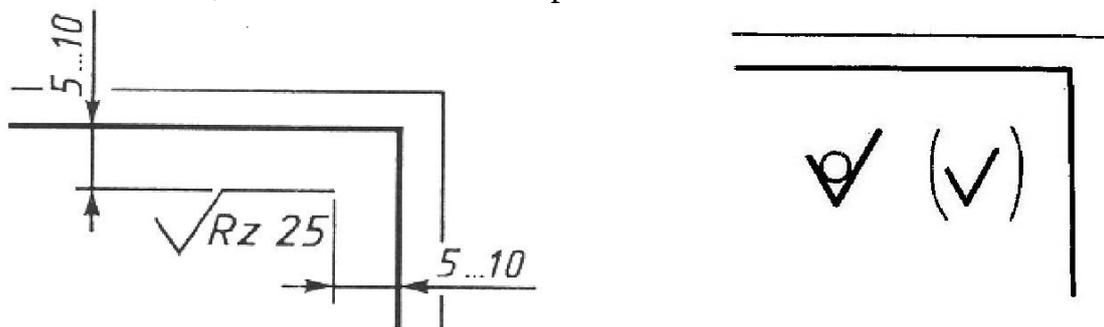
Обозначение одинаковой шероховатости для всех поверхностей
